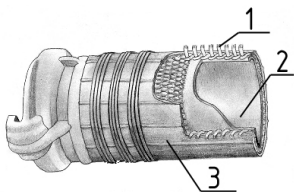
Конструкция напорного рукава с двусторонним покрытием: 1 – армирующий каркас; 2 – внутренний слой; 3 – наружный защитный слой
